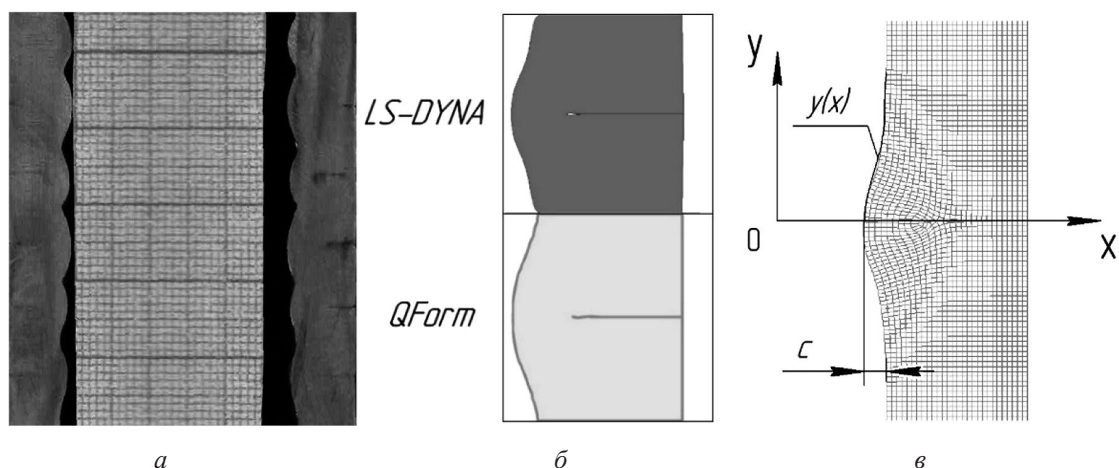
Внешний вид выступов, формируемых при осадке канавок:
